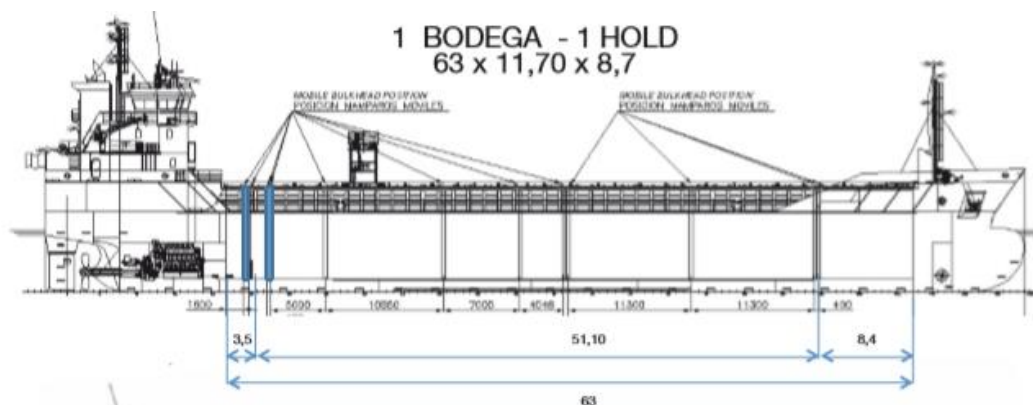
Posición Mamparos Muros, Planos Muros 2008
